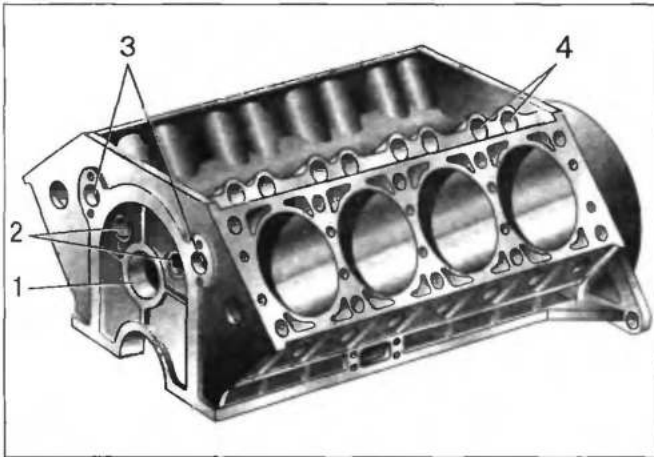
Блок цилиндров двигателя классической американской компоновки V8:
